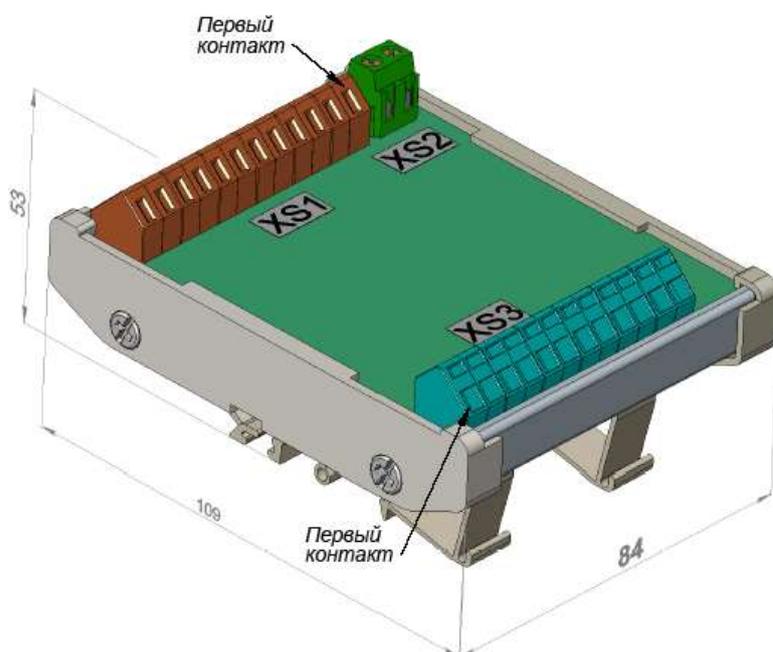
Внешний вид и габаритные размеры барьера ТСС Ex4Т
